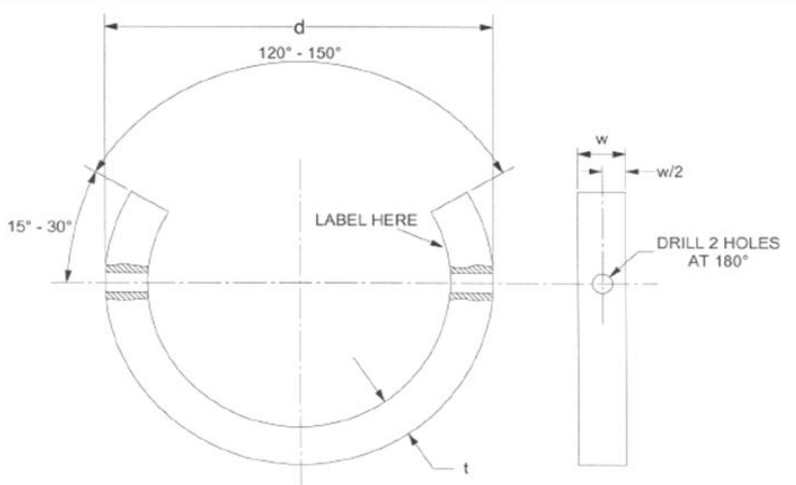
Чертеж испытательного образца С-образного кольца (NACE TM0177-2005)
